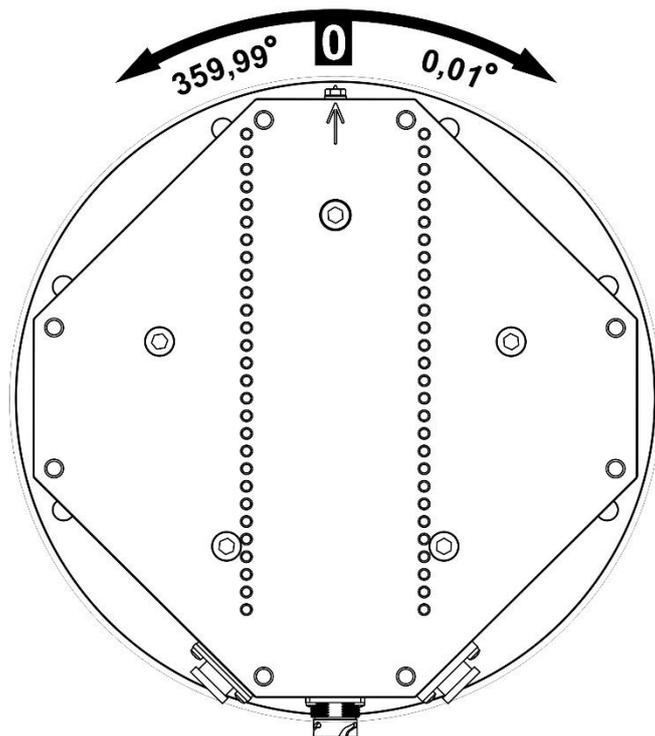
Позиционный чертеж опорно-поворотного устройства (координаты указаны в системе Pelco D)
